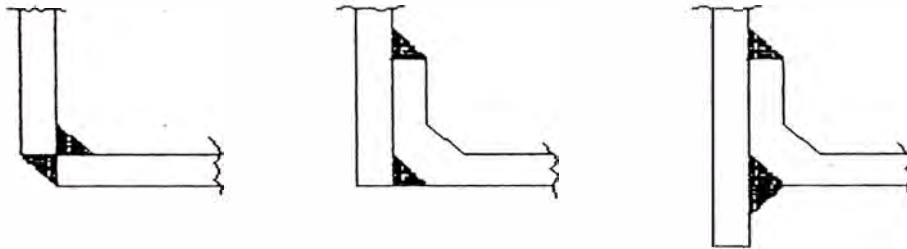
TIPOS DE SOLDADURA PARA PLANCHA
